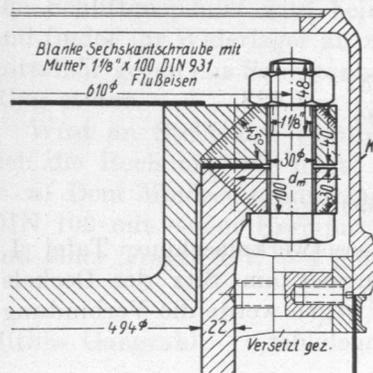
Flanschverbindung mittels Durchsteckschrauben, M. 1:4.
